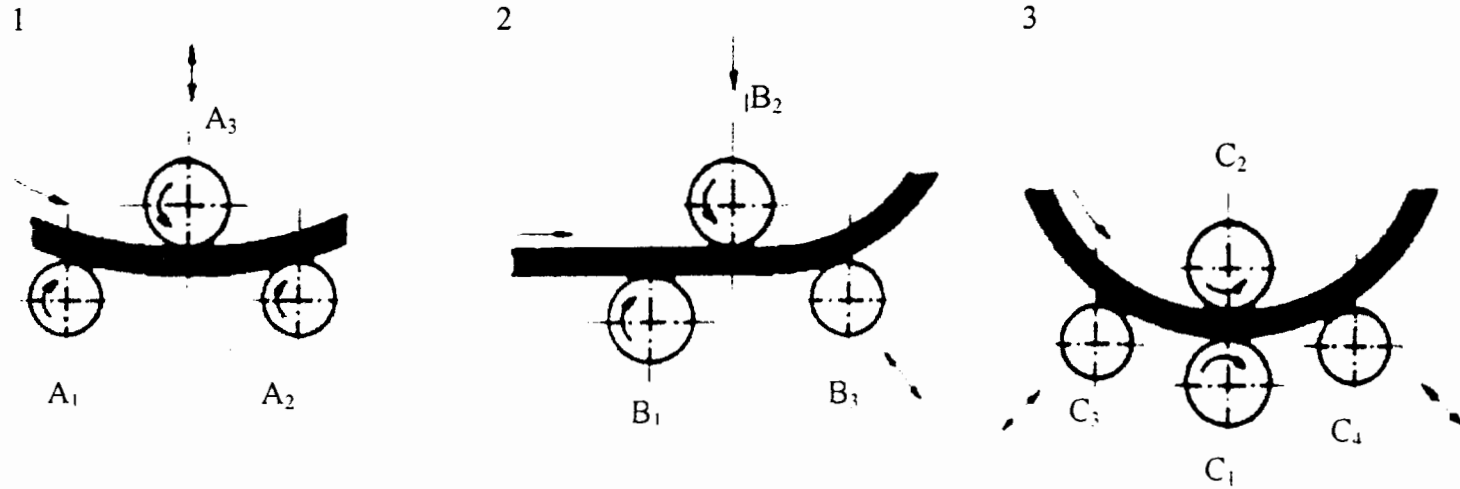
DISPOSICIONES DE LOS CILINDROS DE UNA ROLADORA (REF. 8)
